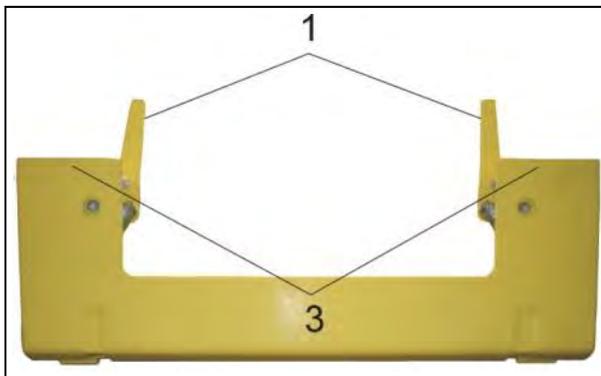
Быстродействующий фиксатор зажима 1- Рычаг, 3- Фиксирующий обод
